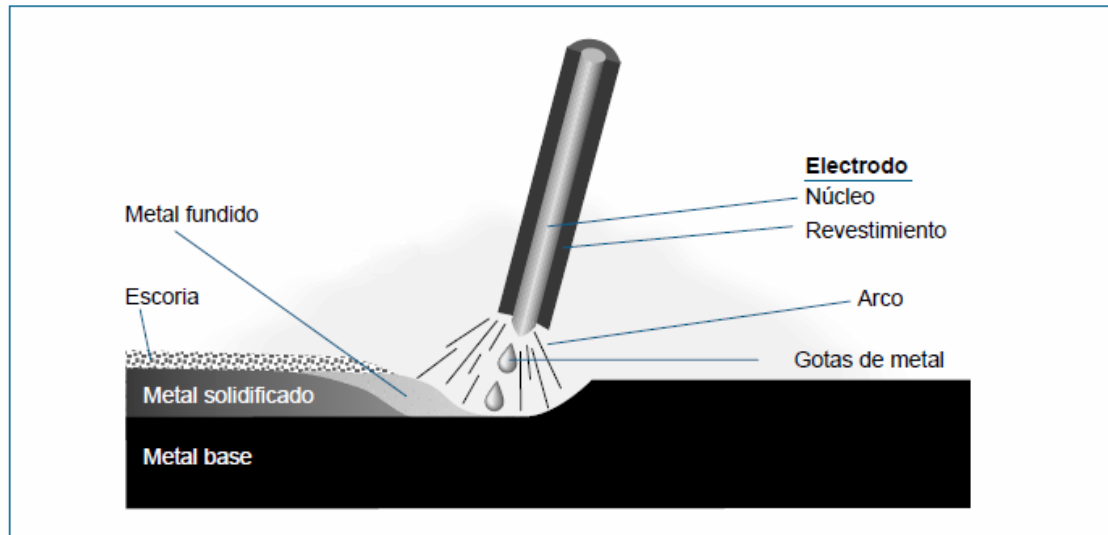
Soldadura por arco con electrodos revestidos
